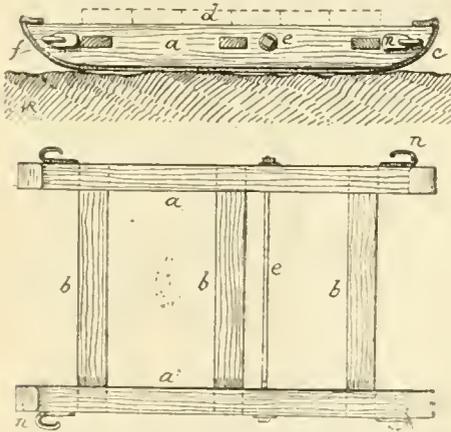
Elevation et plan d'un traîneau à tourner.
